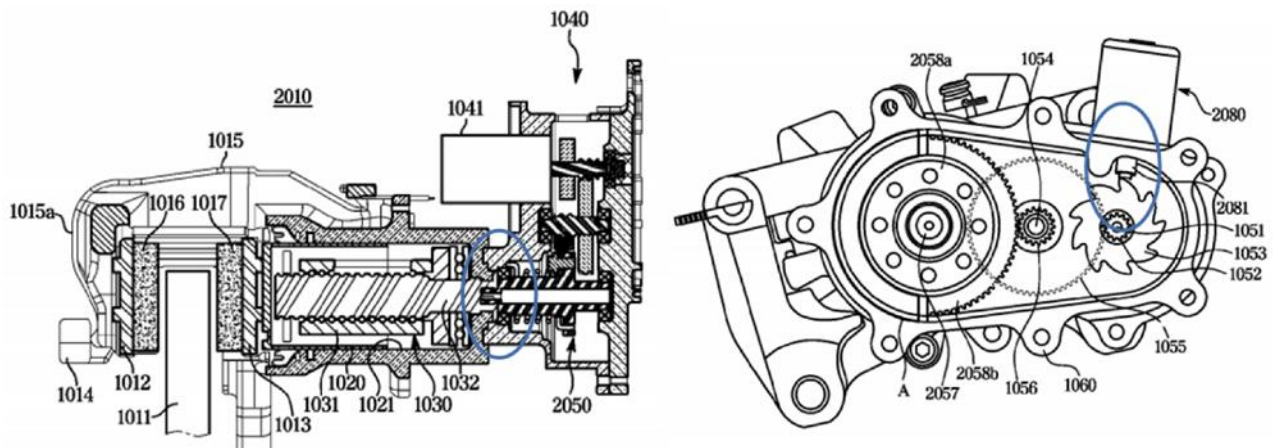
Базова конструкція приводу EMB Mando
